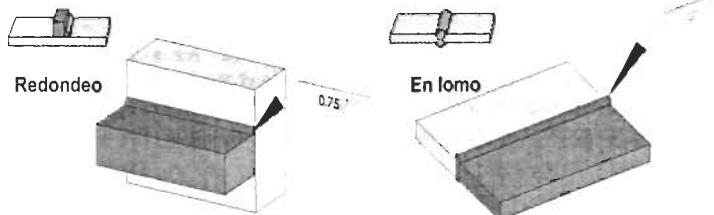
Creación de Cordones de soldadura entre dos componentes de un ensamblaje.
